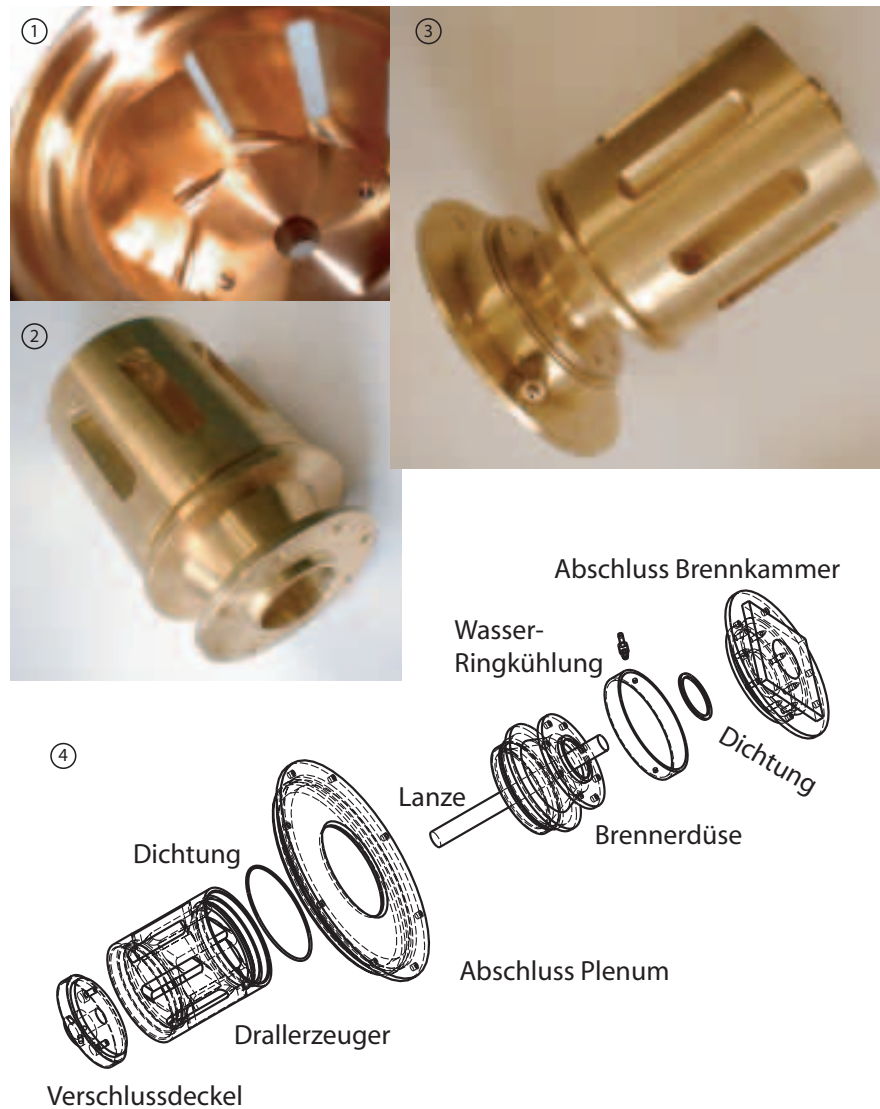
① Innenansicht Drallerzeuger, ② Drallerzeuger und Brennerdüse, ③ TD¹ Brenner, ④ Explosionszeichnung mit Bauteilbezeichnungen.
